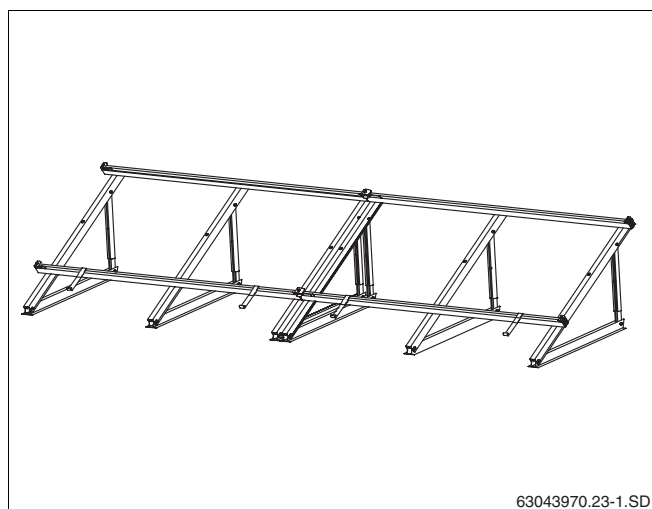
Suportes horizontais para telhados planos para 2 colectores
